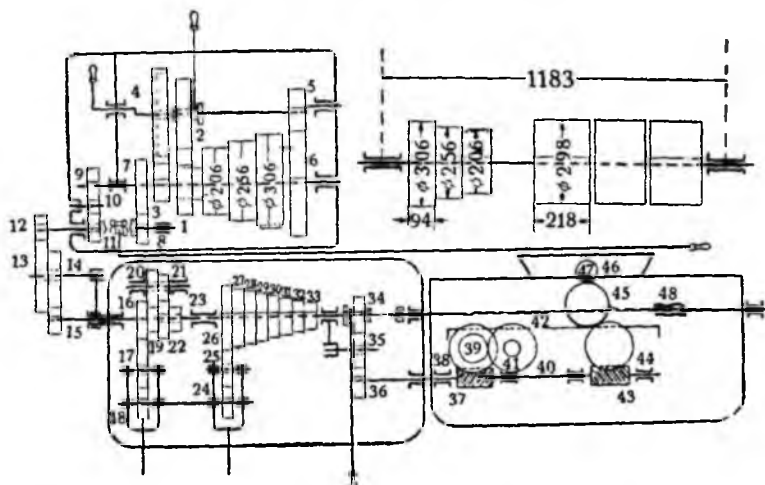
Кинематическая схема станков ТН-20 и ТН-27.
